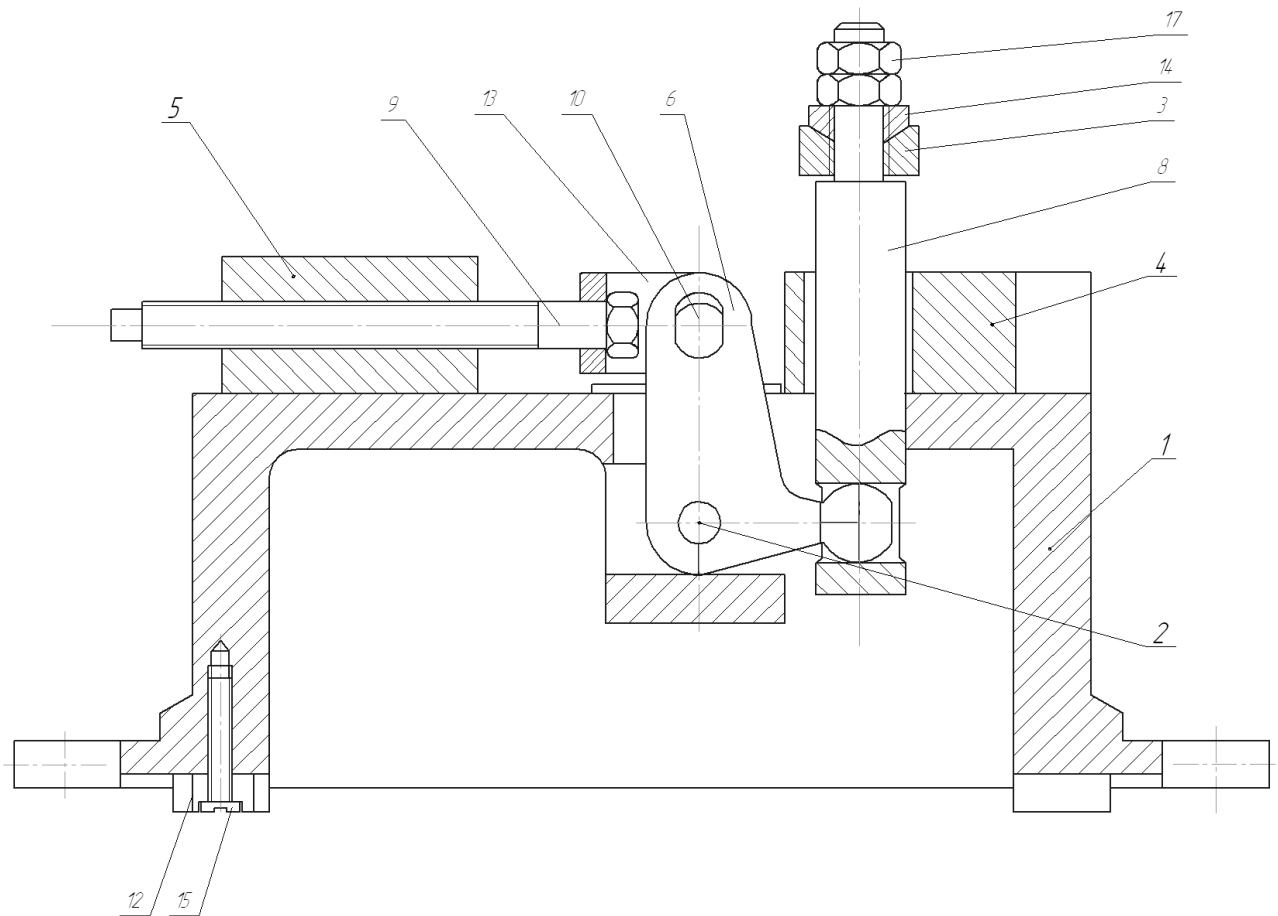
Приспособлення для фрезерування шпонкових пазів.
